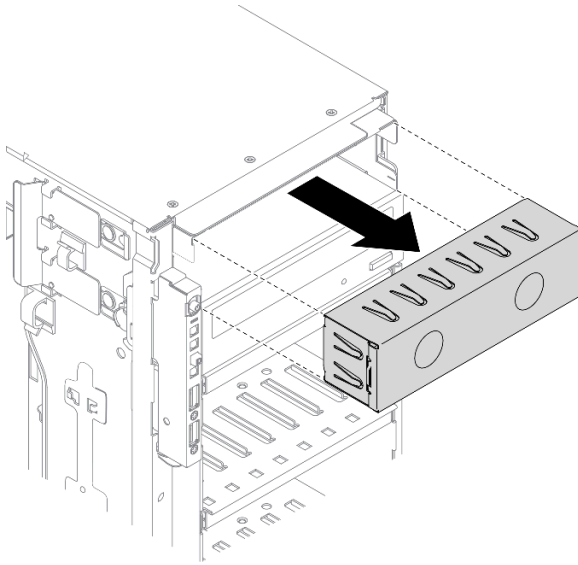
Installation der Abdeckblende für die Laufwerkposition
